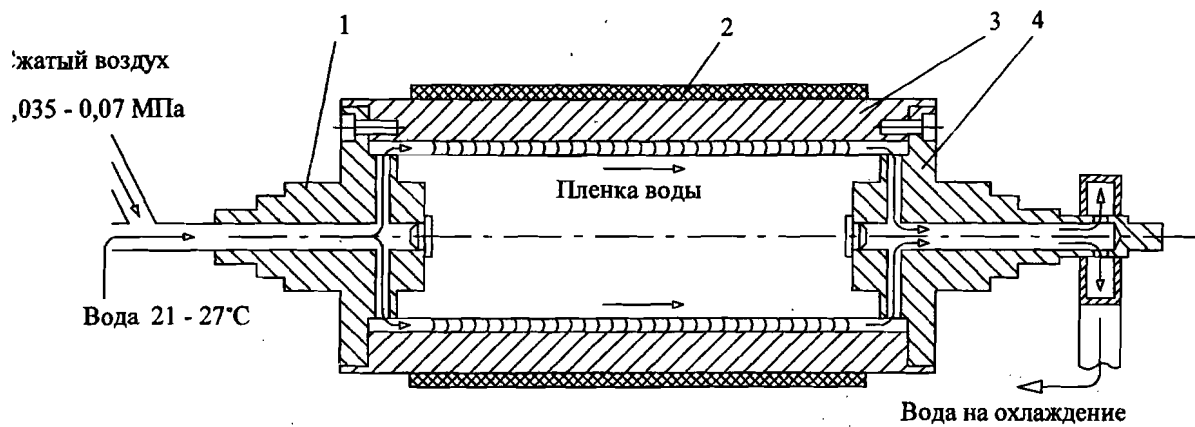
Прессовый вал с внутренним водяным охлаждением: 1 – цапфа левая; 2 – резиновое покрытие; 3 – рубашка вала; 4 – цапфа правая
